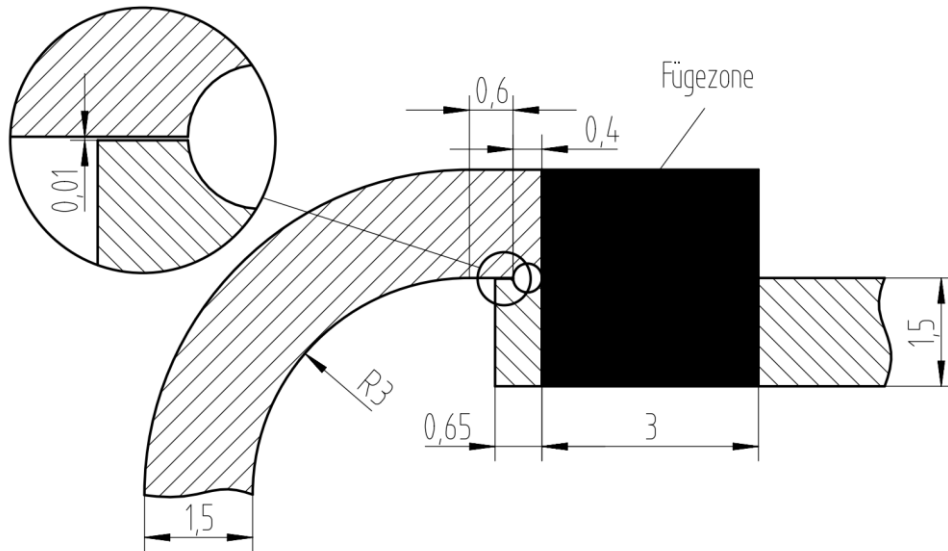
Schweißnahtgeometrie am Rohranschluss
